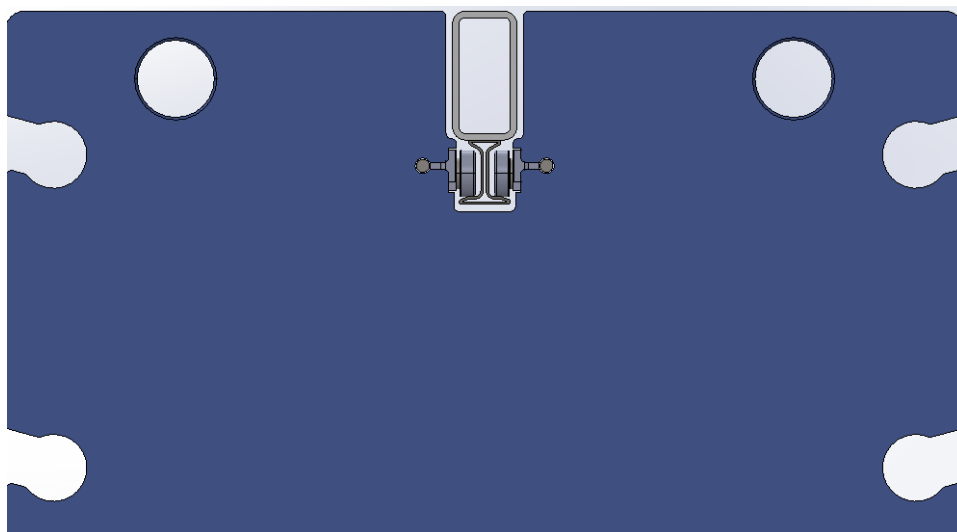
Detalhe dos rolamentos na calha soldada ao tirante superior.
